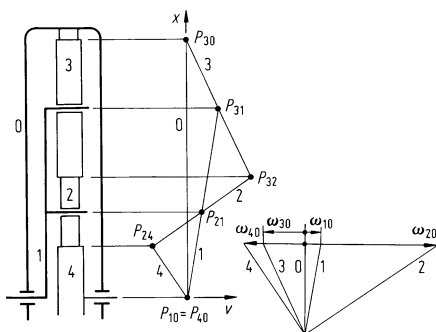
Bauplan eines Planetenradgetriebes (links) mit Geschwindigkeitsplan (Mitte) und Winkelgeschwindigkeitsplan (rechts) für stehendes Gehäuse 0
